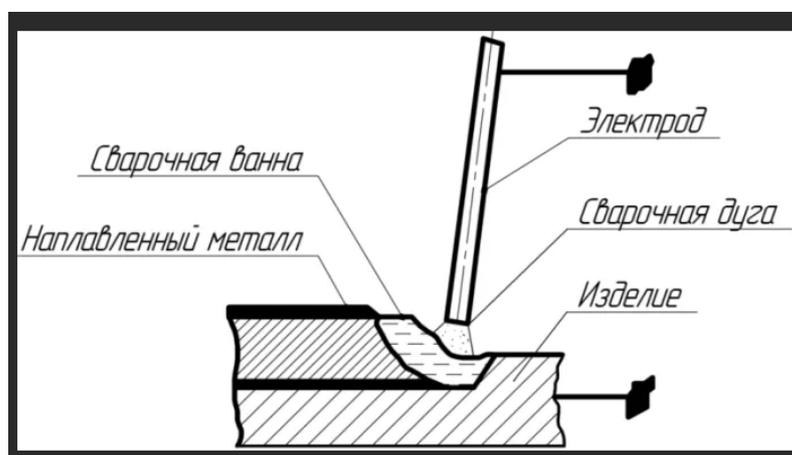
Схема ручной дуговой наплавки покрытыми электродами
